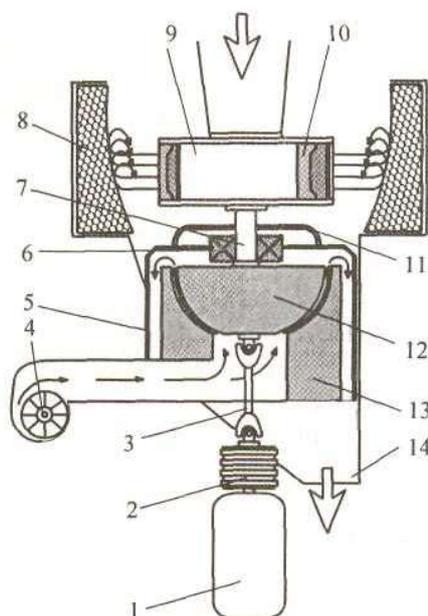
Схема дробилки ООО "НТ" 1 - электродвигатель; 2 - центробежная муфта; 3 - карданный вал; 4 - вентилятор воздуха; 5 — крышка опорной части; 6 — предохранительный узел на случай аварийного отключения подачи воздуха; 7 - вал; 8 - камера измельчения; 9 - ускоритель; 10 - концевая лопатка ускорителя; 11 - пыльник; 12 - ротор; 13 - статор; 14 – патрубок для выгрузки дробленого продукта.
